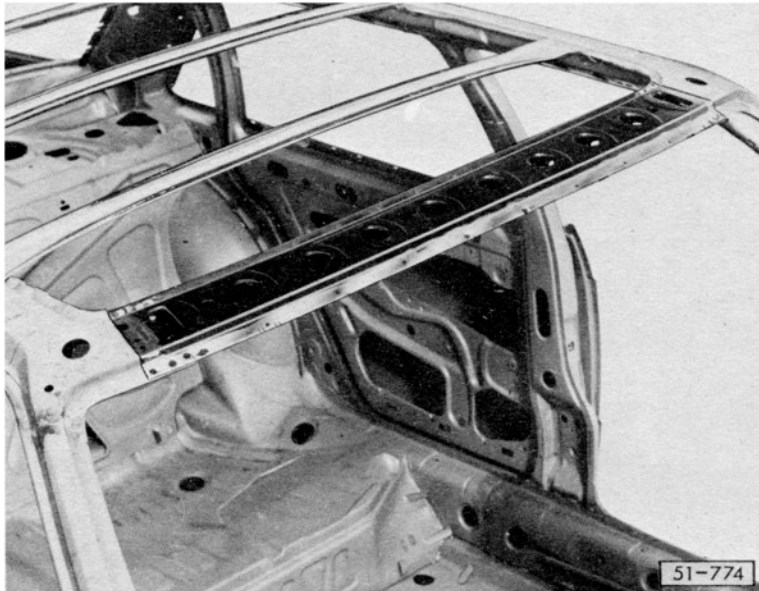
Querträger für Dach vorn einschweißen.
